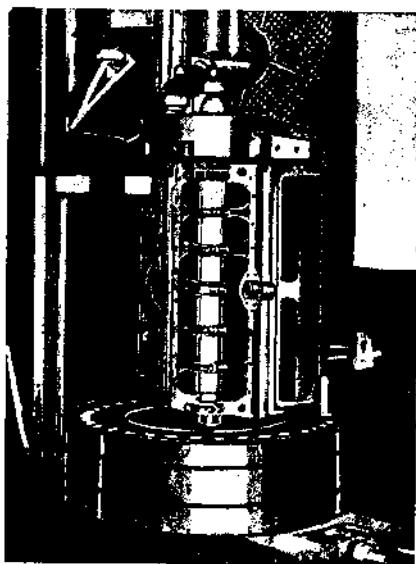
Специальный станок Ньютон для фрезеровки углубления для маховика.
